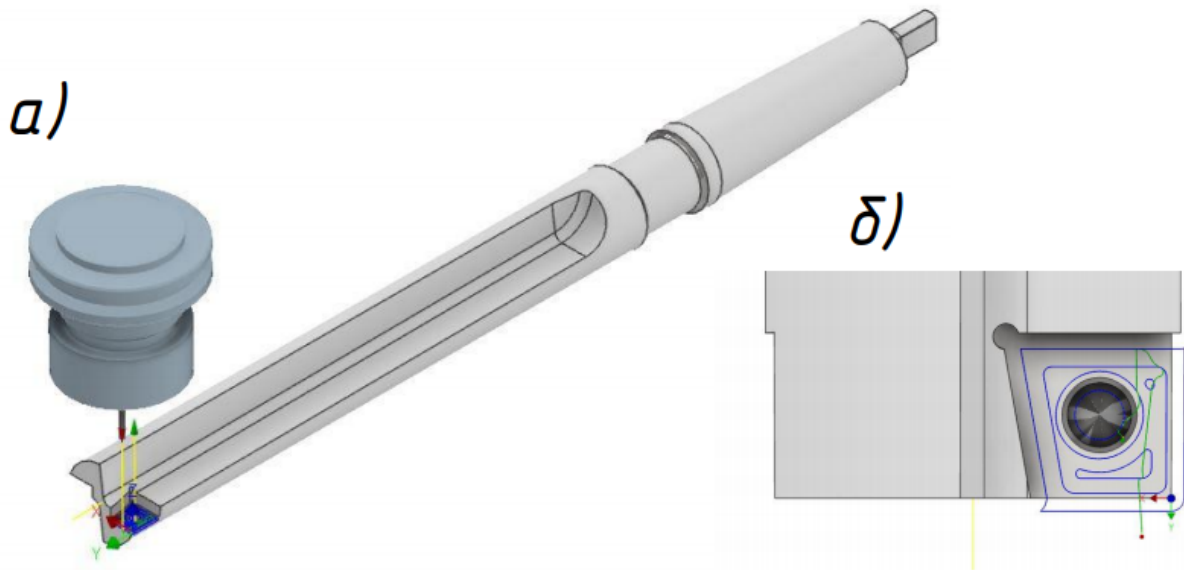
Фрезерування пазу під пластину на верстаті з ЧПК:
